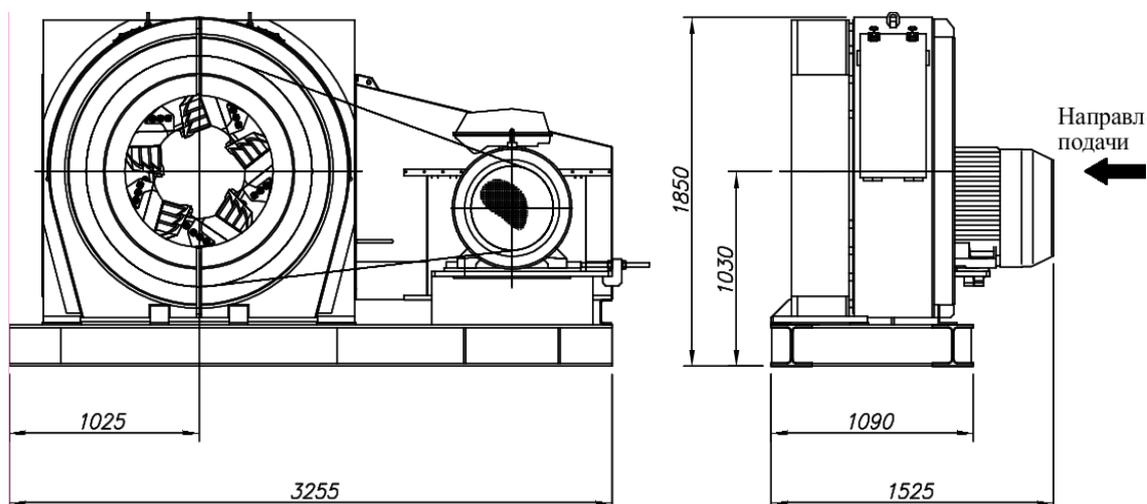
Габаритные размеры станка для оцилиндровки марки CamTrim
